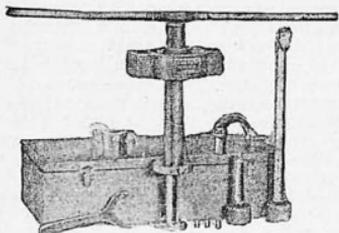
Части прибора Х. Майерс для ручной расточки цилиндров
